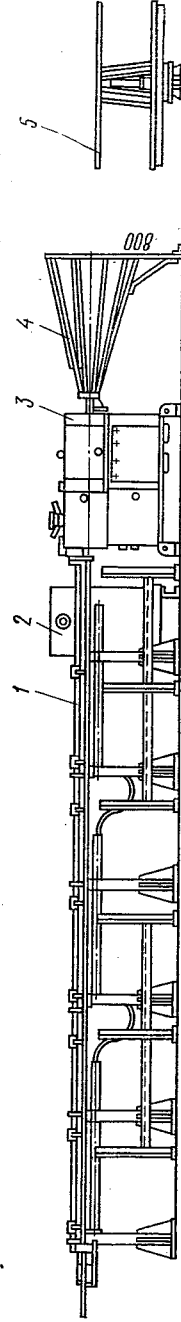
Установка СМЖ-357 для правки и резки арматурной стали:
